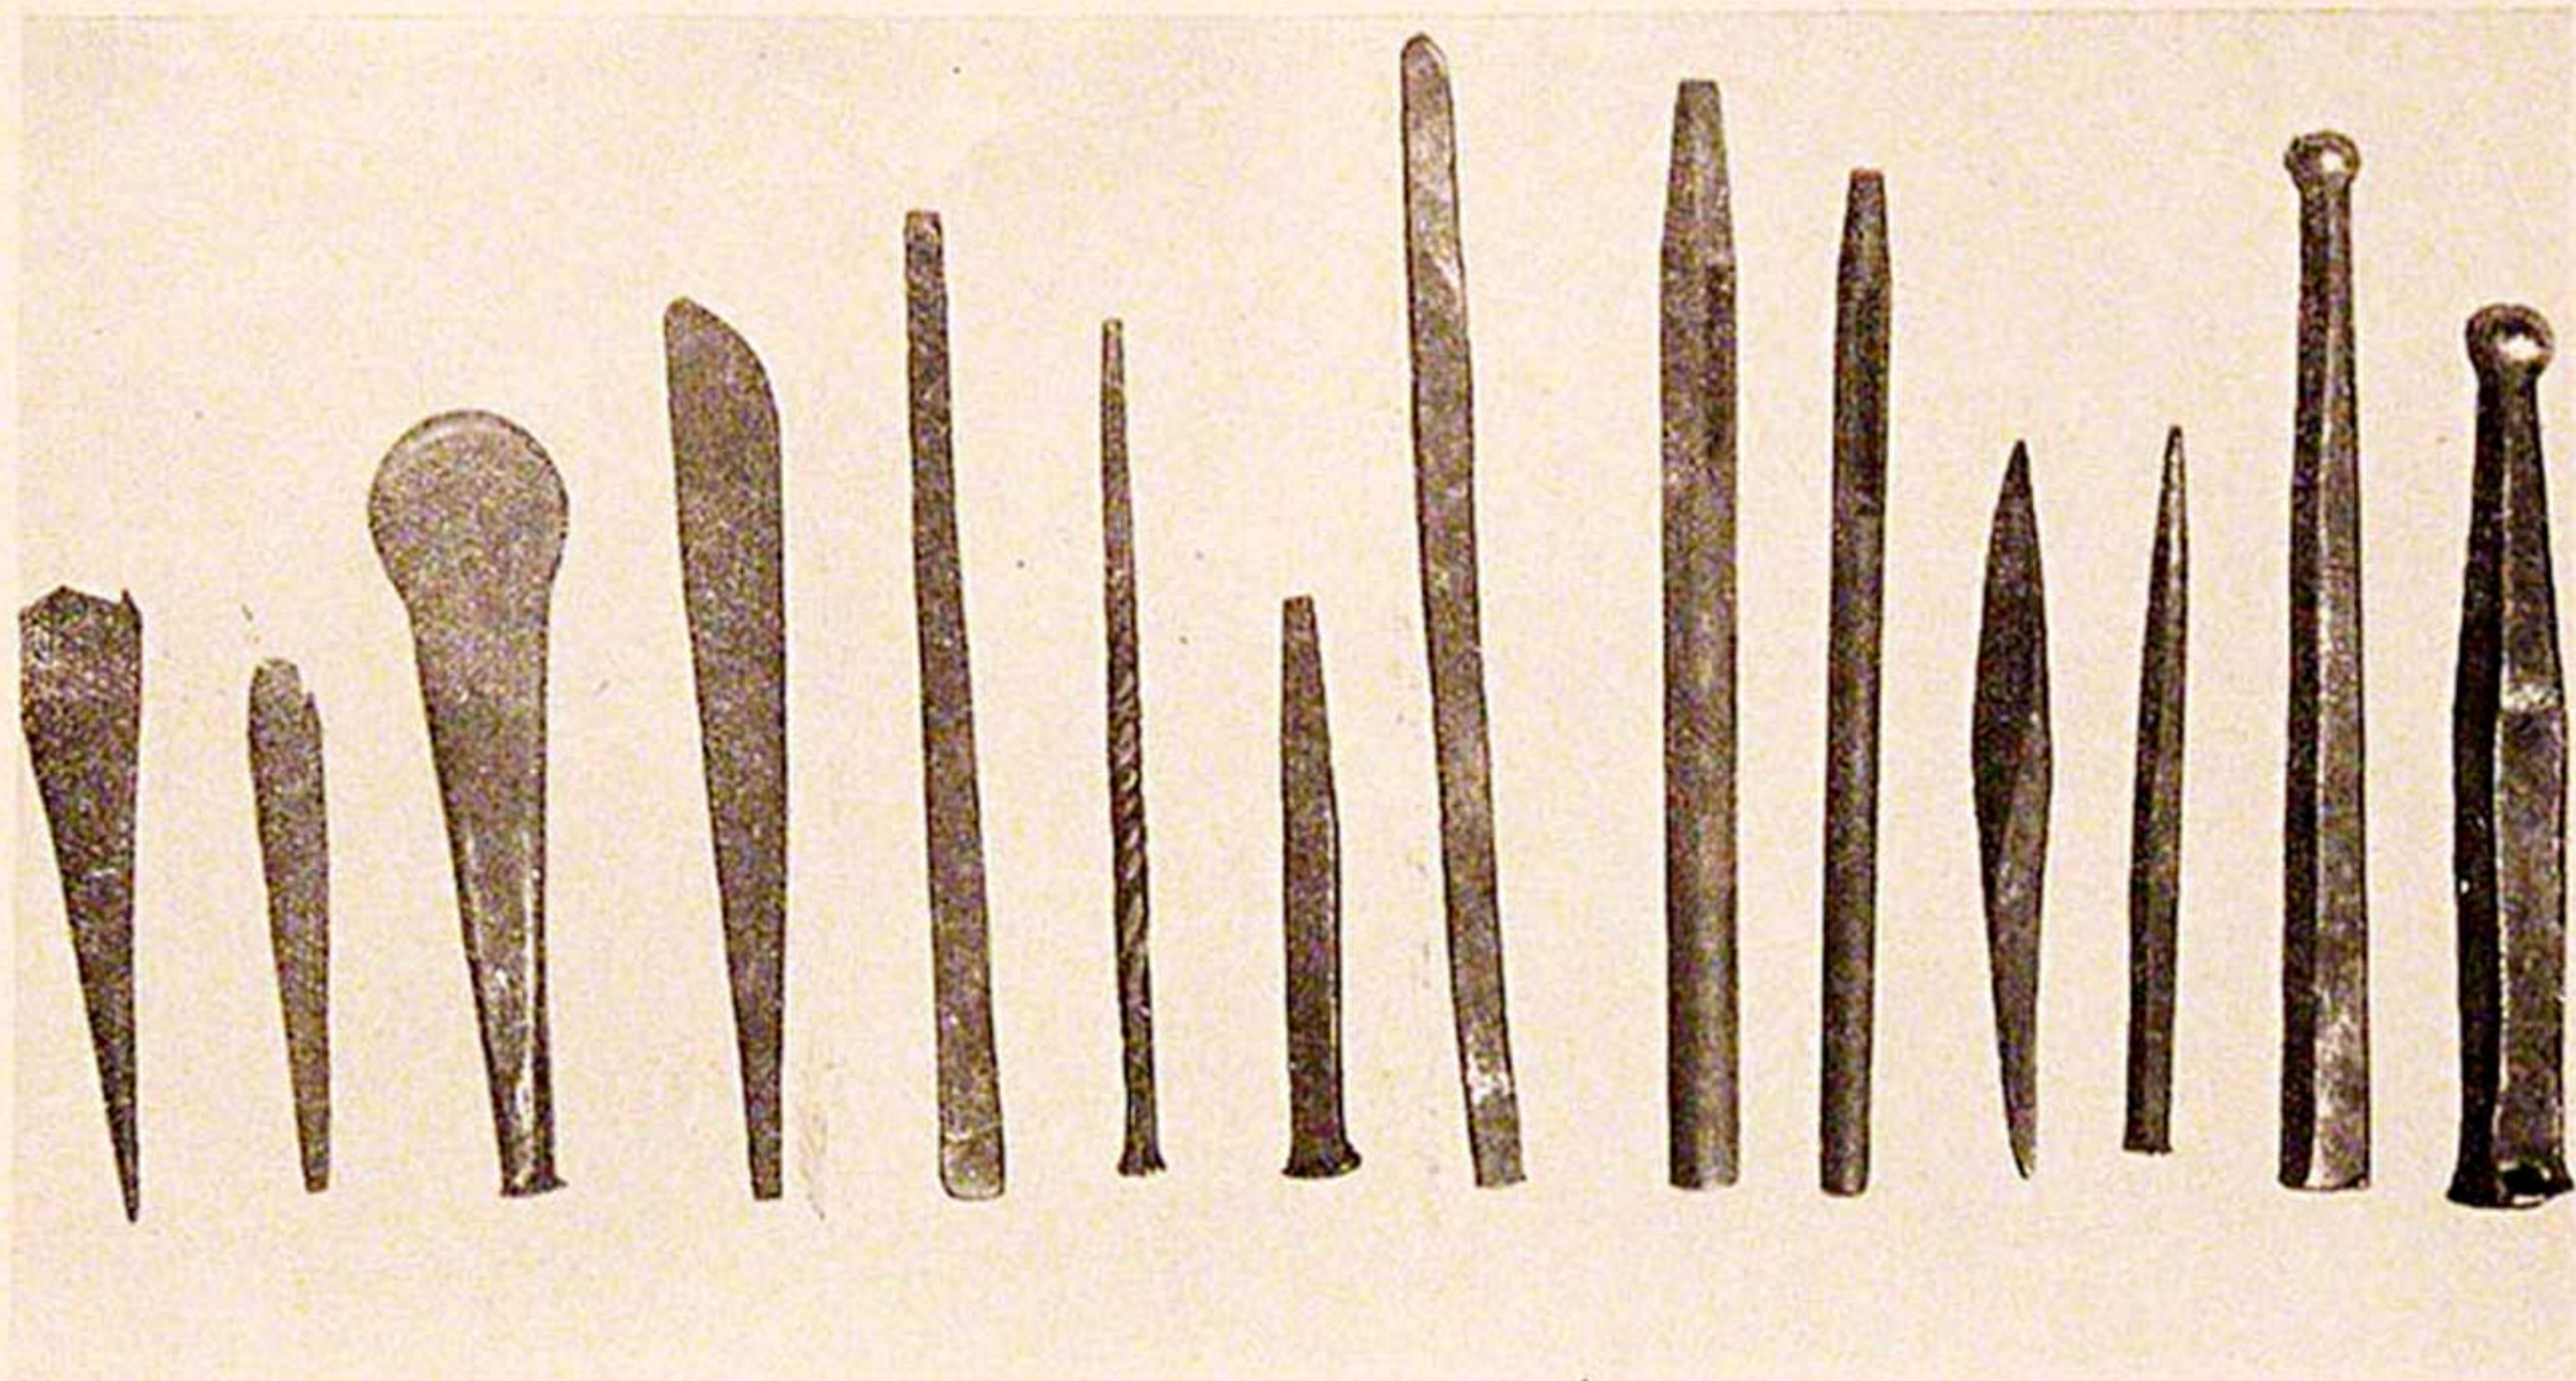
Инструменты ювелира. Набор стамесок (қалам) для чеканки и резьбы. Фото.
